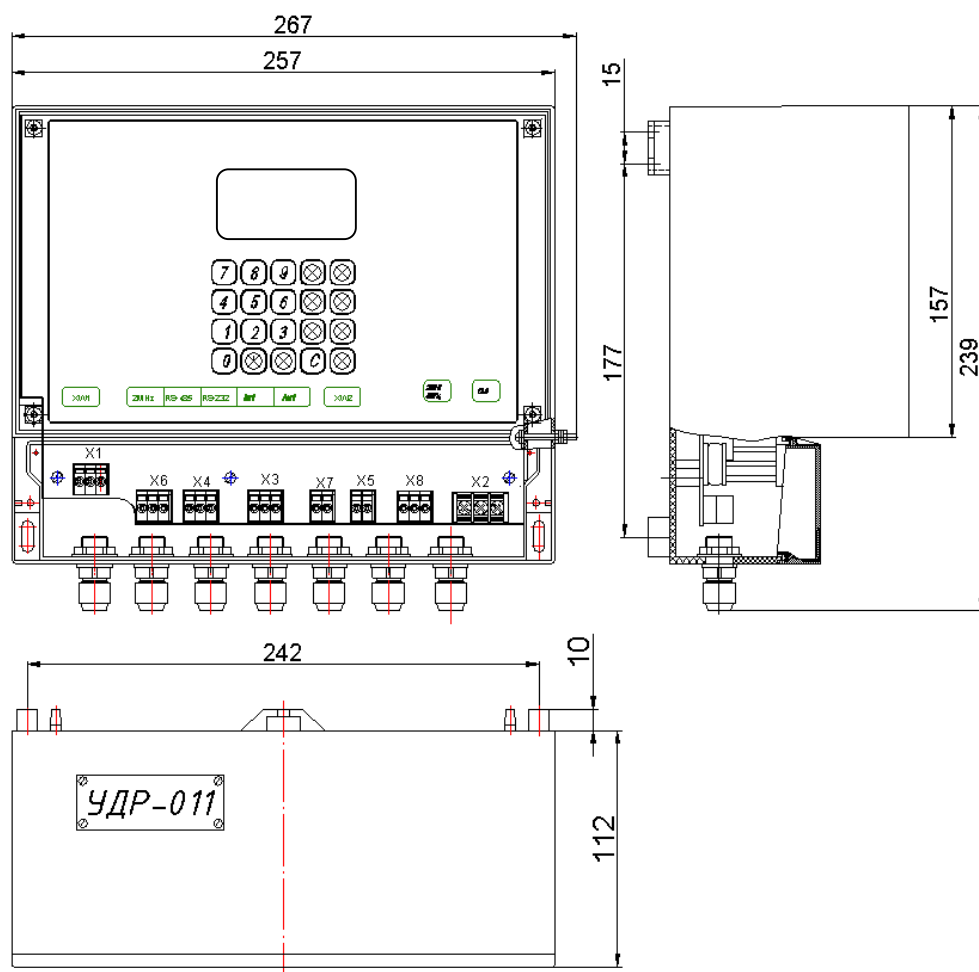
Внешний вид, габаритные и установочные размеры УДР-011-БЭ
